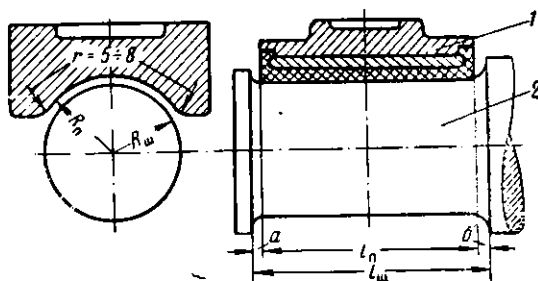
Схема правильного расположения подшипника на шейке оси:
